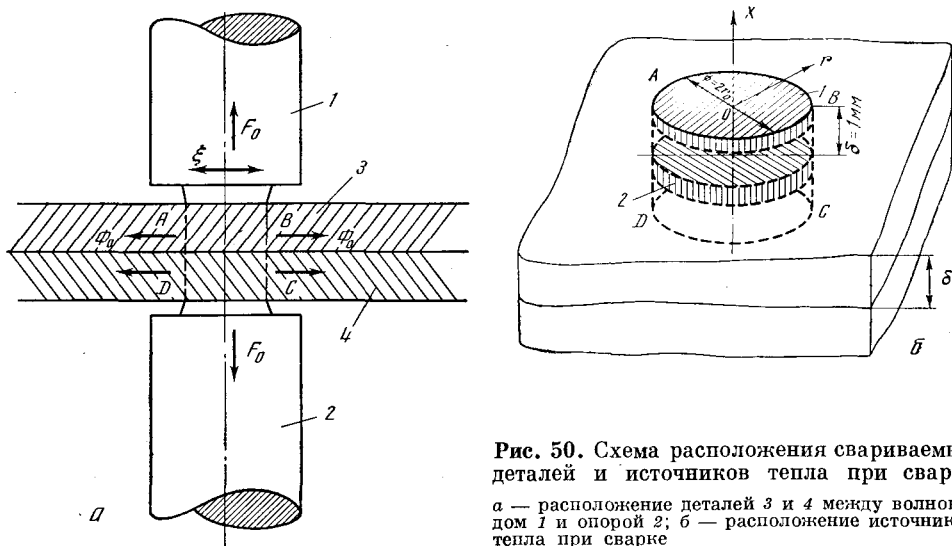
Схема расположения свариваемых деталей и источников тепла при сварке
